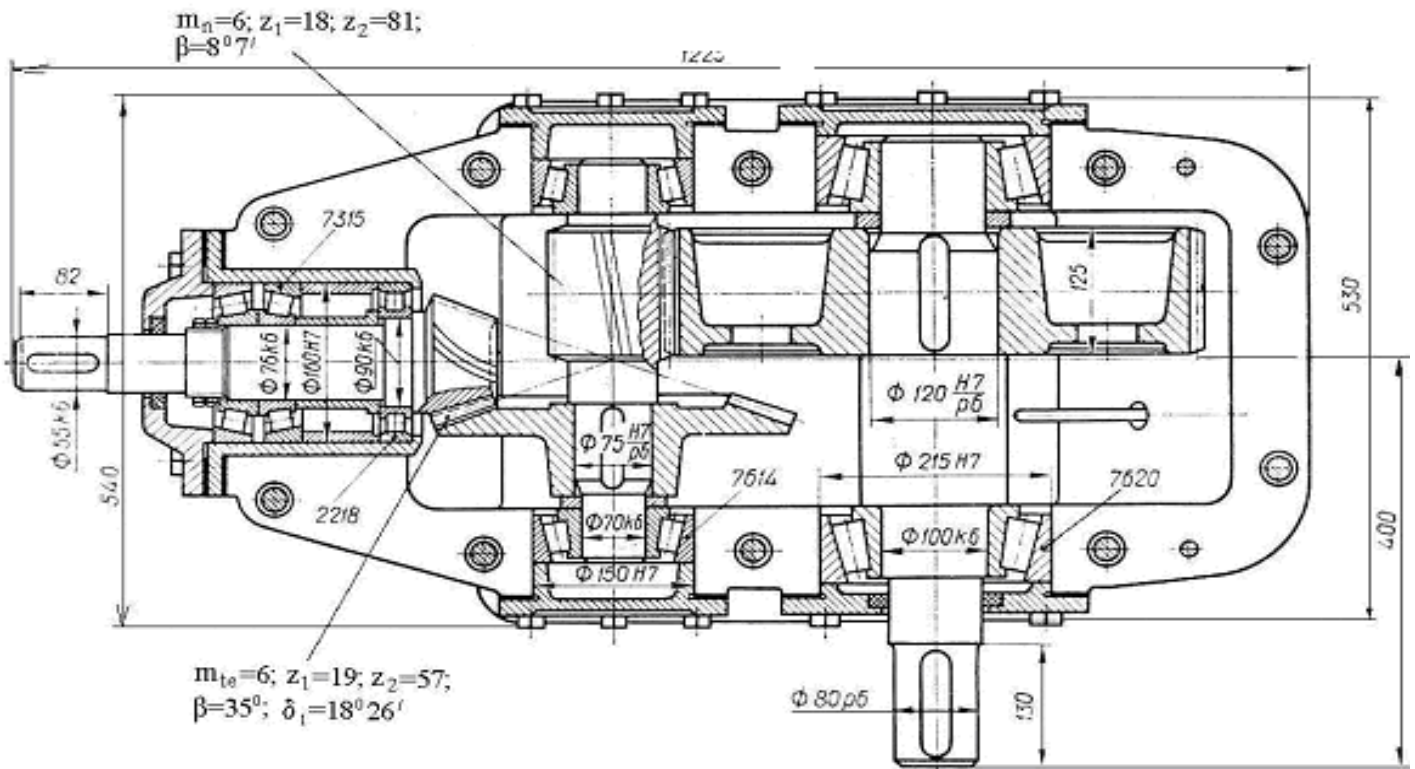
,в. Вид зверху на редуктор конічно-циліндричний
